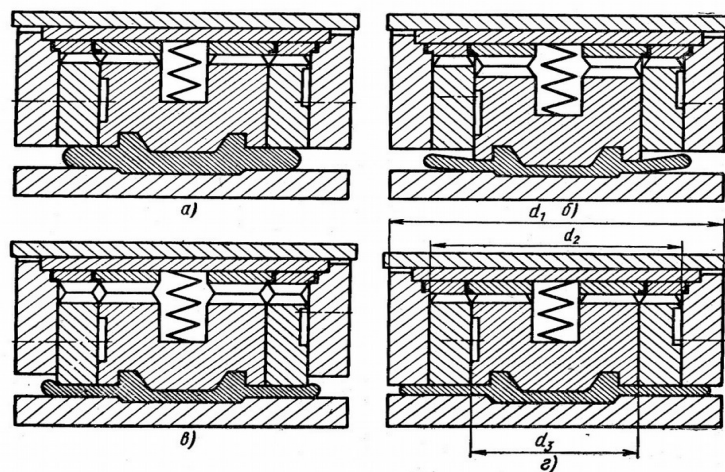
Схема изготовления поволок дисков трехсекционным инструментом:
